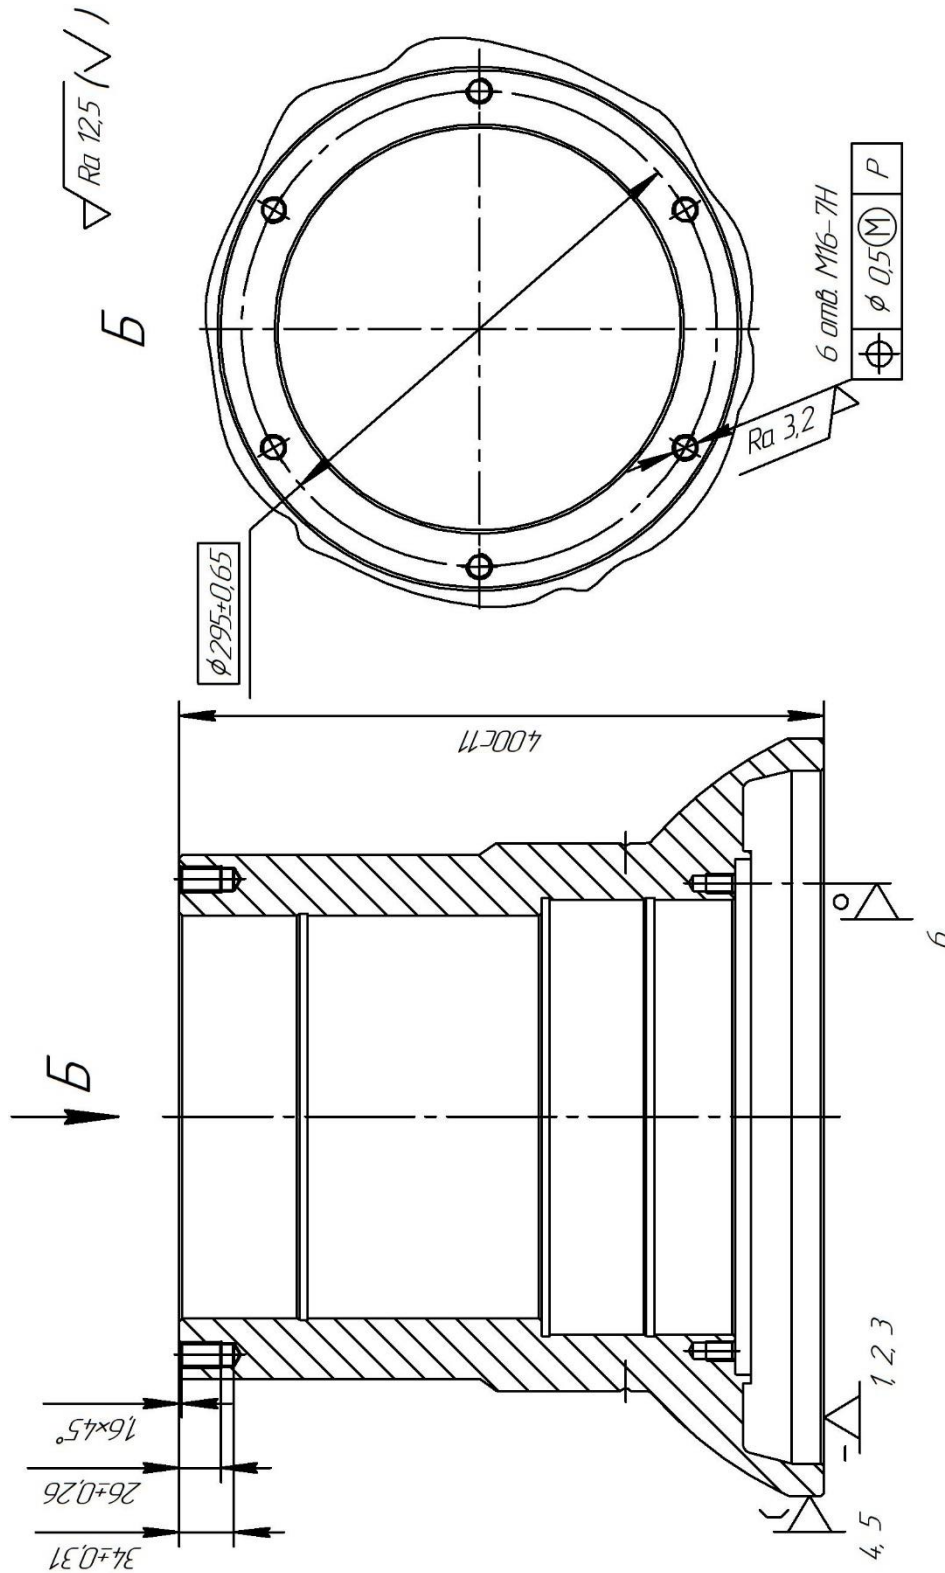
Схема базування заготовки на операції радіально-свердильній 050 (установ Б)
